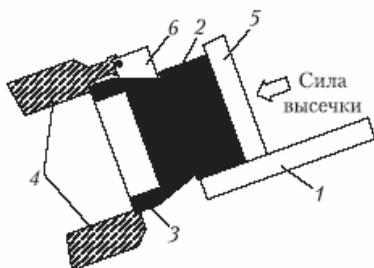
Высекальное устройство: 1 — лоток подачи; 2 — стопа прямоугольных заготовок материала; 3 — штамп; 4 — штамподержатель; 5 — прессующая плита; 6 — разделительный нож
